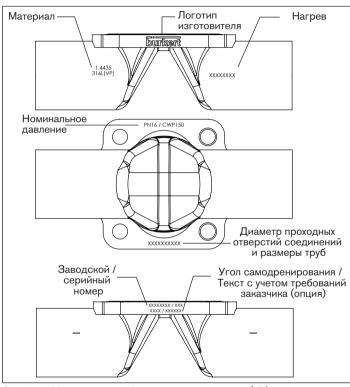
Маркировка трубчатого корпуса клапана (VP)
